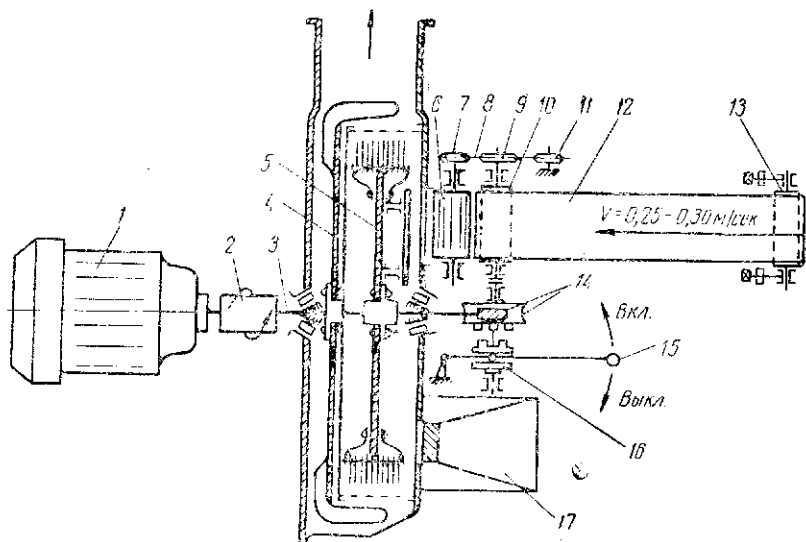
Кинематическая схема универсальной дробилки кормов ДКУ-М:
